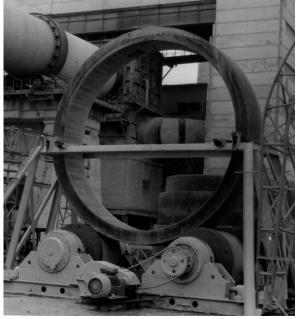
Бандаж, установленный на специальный стенд для обработки торцевых поверхностей (операция 020)
